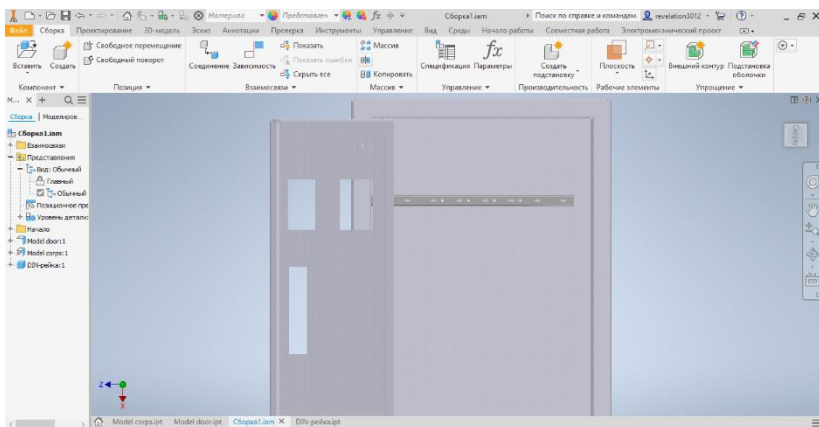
Видяк закріпленої DIN-рейки на корпусі
